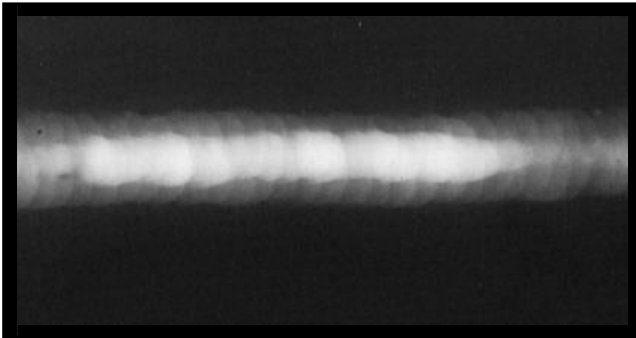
Radiografía obtenida con la PVI mostrando una soldadura con exceso de penetración.
